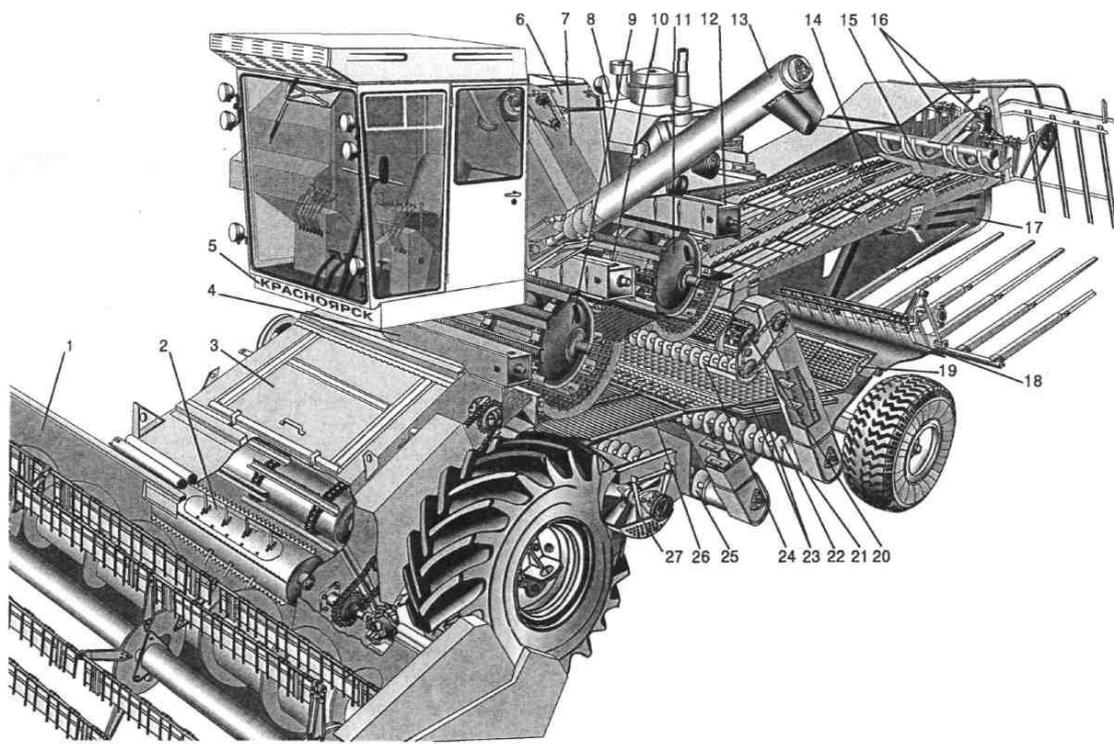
Устройство зерноуборочного комбайна «Енисей-1200М»: 1 – жатка; 2 – бита проставки; 3 – наклонная камера; 4 – приемный бита; 5 – кабина; 6 – зерновой бункер; 7 – зерновой элеватор; 8 – двигатель; 9 – первый молотильный барабан; 10 – промежуточный бита; 11 – второй молотильный барабан; 12 – отбойный бита; 13 – выгрузной шнек; 14 – соломотряс; 15 – щиток сброса соломы; 16 – граблины соломонабивателя; 17 – копнитель; 18 – половонабиватель; 19 – удлинитель верхнего решета; 20 – домолачивающее устройство; 21 – колосовой элеватор; 22 – колосовой шнек; 23 – верхнее и нижнее решета очистки; 24 – распределительный шнек домолачивающего устройства; 25 – зерновой шнек; 26 – трясная доска грохота; 27 – вентилятор очистки
